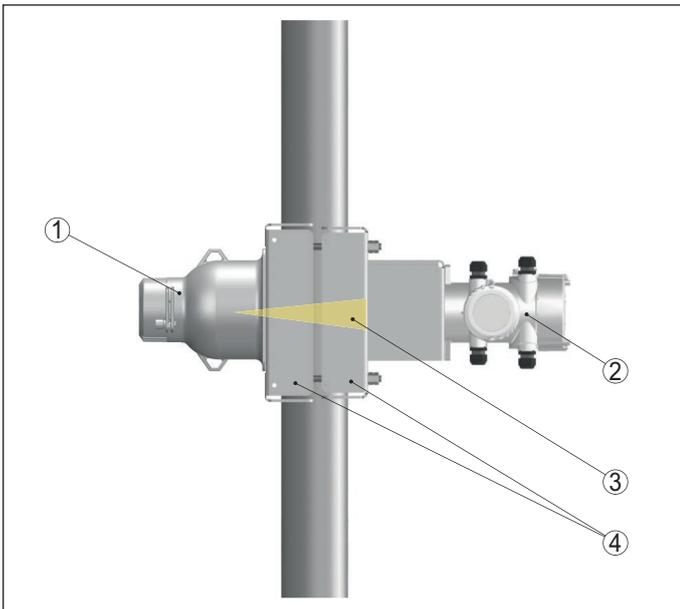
Dispositivo di fissaggio per montaggio su tubi da 50 ... 220 mm (1.97 ... 8.66 in)
